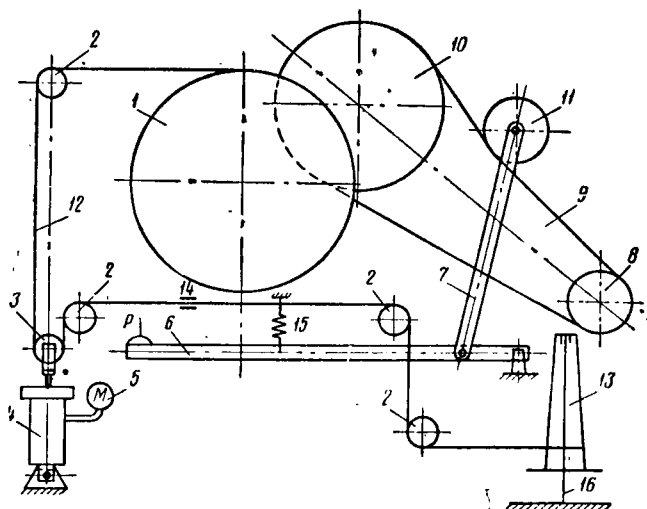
Кинематическая схема натяжного устройства бандажировочного станка:
